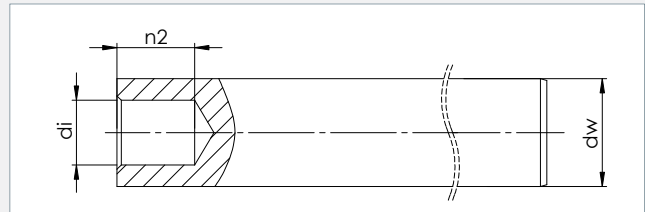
Zusammengesetzte Wellen / Compound shafts
